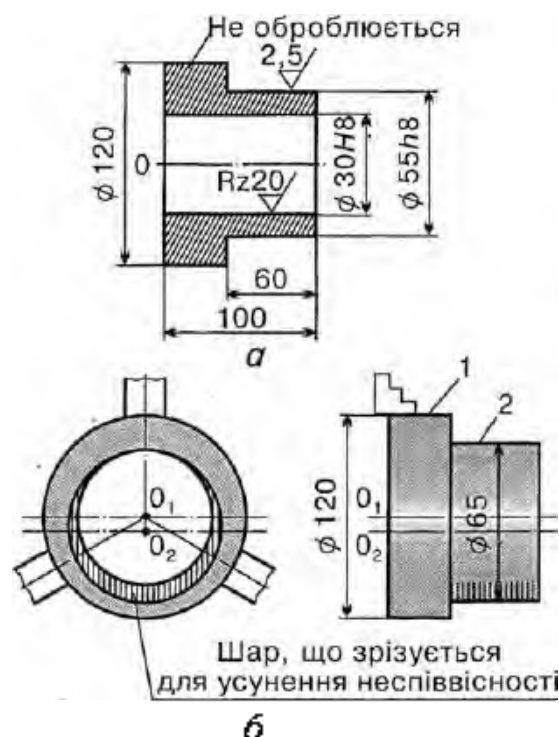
ПРИКЛАД ВИБОРУ ЧОРНОВОЇ БАЗИ
